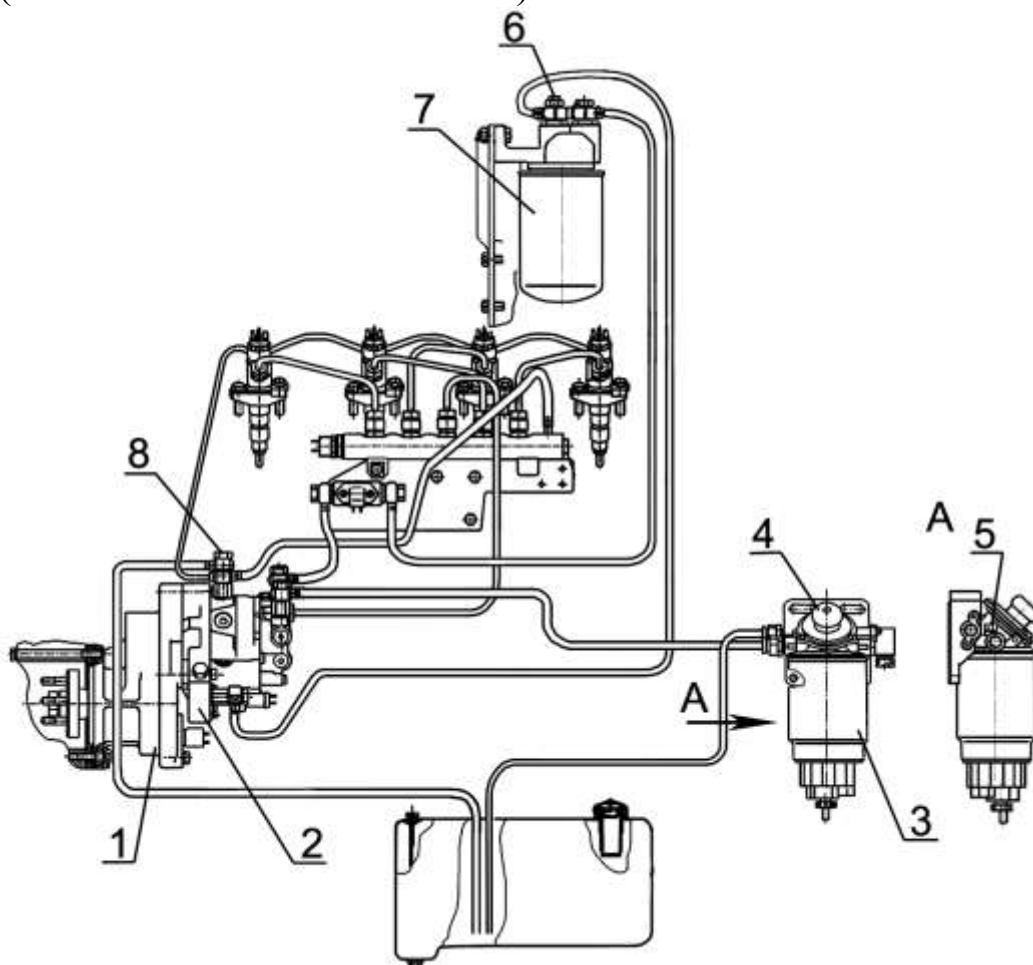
Удаление воздуха из топливной системы: 1- редуктор; 2 - насос топливный; 3 – фильтр грубой очистки топлива; 4 – ручной подкачивающий насос; 5 – пробка для выпуска воздуха; 6 – пробка; 7 – фильтр топливный тонкой очистки; 8 – болт поворотного угольника
